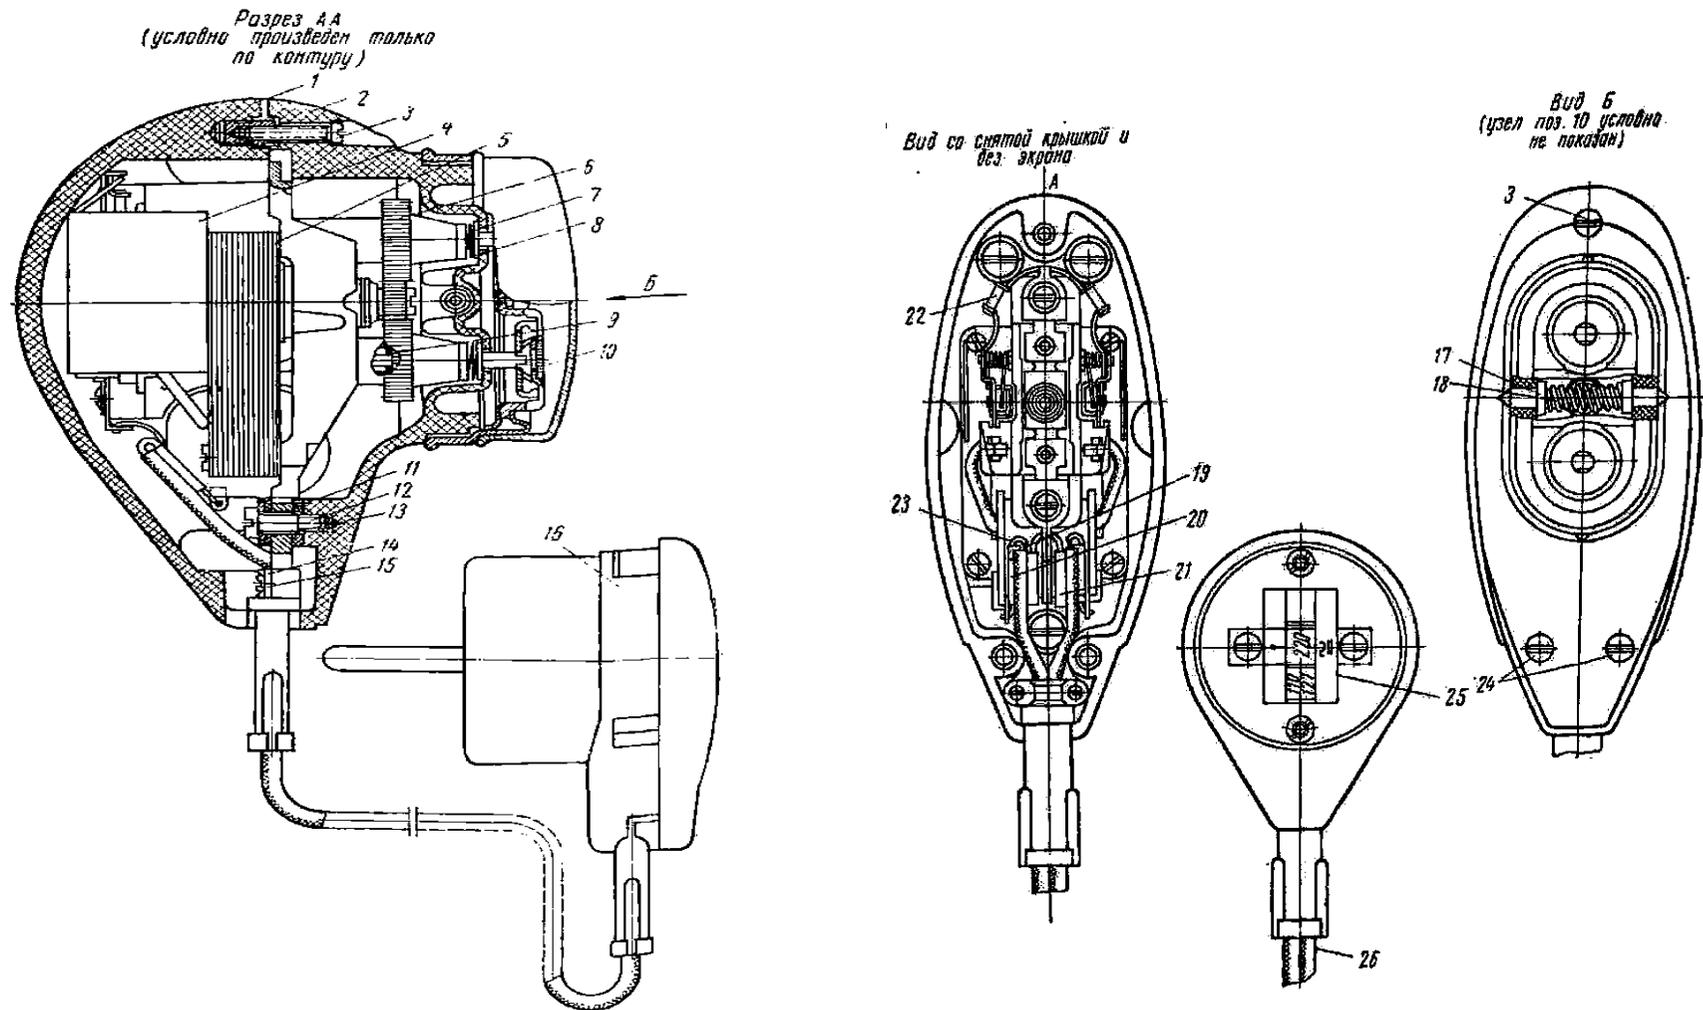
Электрическая бритва «Москва ИП-6»: 1 – крышка; 2 – корпус; 3, 12, 15, 24 - винты; 4 – экран; 5 – электродвигатель; 6 – зубчатое колесо; 7, 18 - пружины; 8, 9, 11 – прокладки; 10 – ножевой блок; 13 – шайбы; 14 – планка; 16 – штепсельная вилка с переключателем напряжения; 17 – фиксатор; 19 дроссель ферритовый; 20, 23 – трубки изоляционные; 21, 22 – конденсаторы; 25 – переключатель напряжения; 26 – соединительный шнур.
